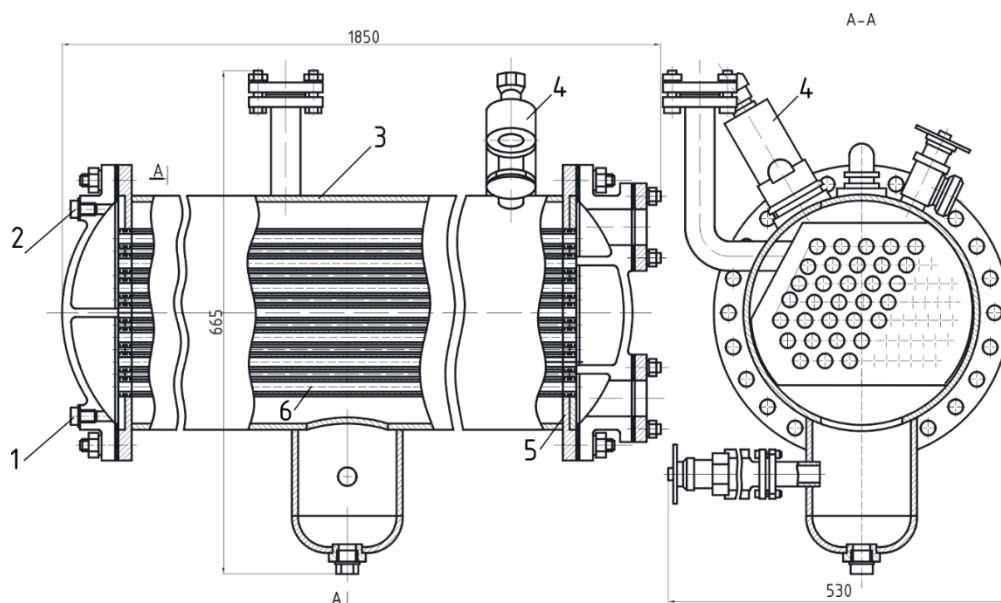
Горизонтальний кожухотрубний хладоновий конденсатор [12]:
